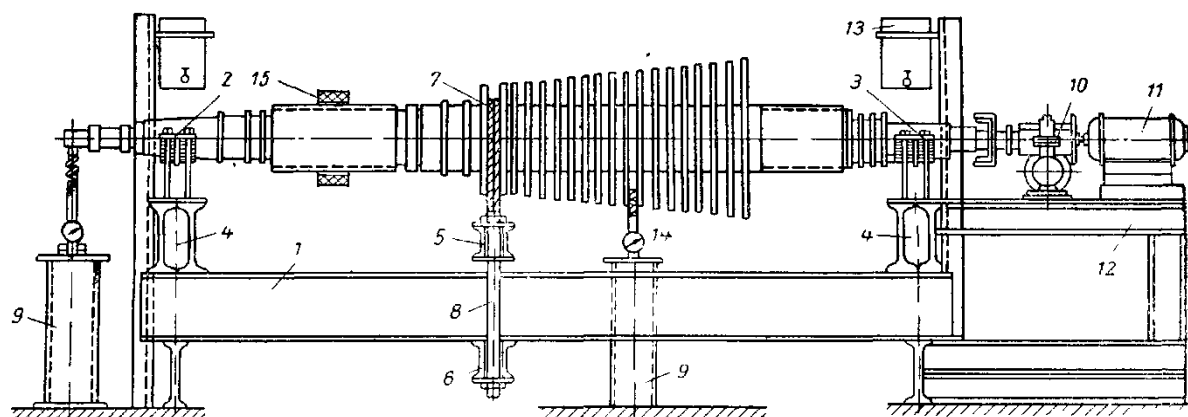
Правка вала способом релаксации. 1—станина, 2 и 3—подшипники, 4—опоры подшипников, 5 и 6—траверсы; 7—нажимной трос, 8—стяжной болт, 9—подставка для индикатора, 10—редуктор, 11—электромотор, 12—опора привода, 13—сосуд для смазочного масла, 14—индикатор, 15—индукционный нагреватель.
